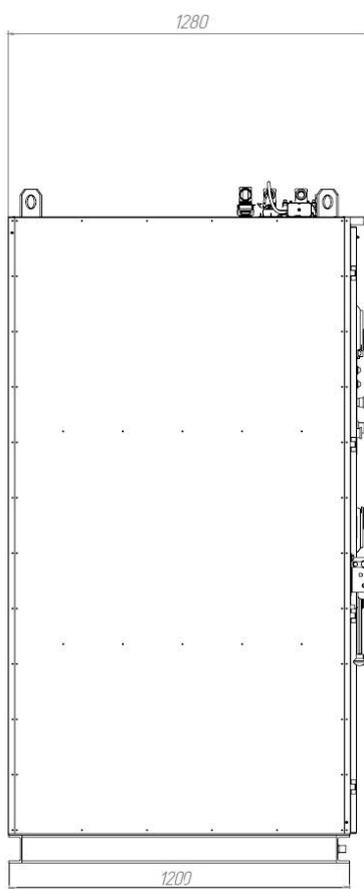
АТ27-М40...М63-6/6-XXXXXX-С-43. Вид сбоку
